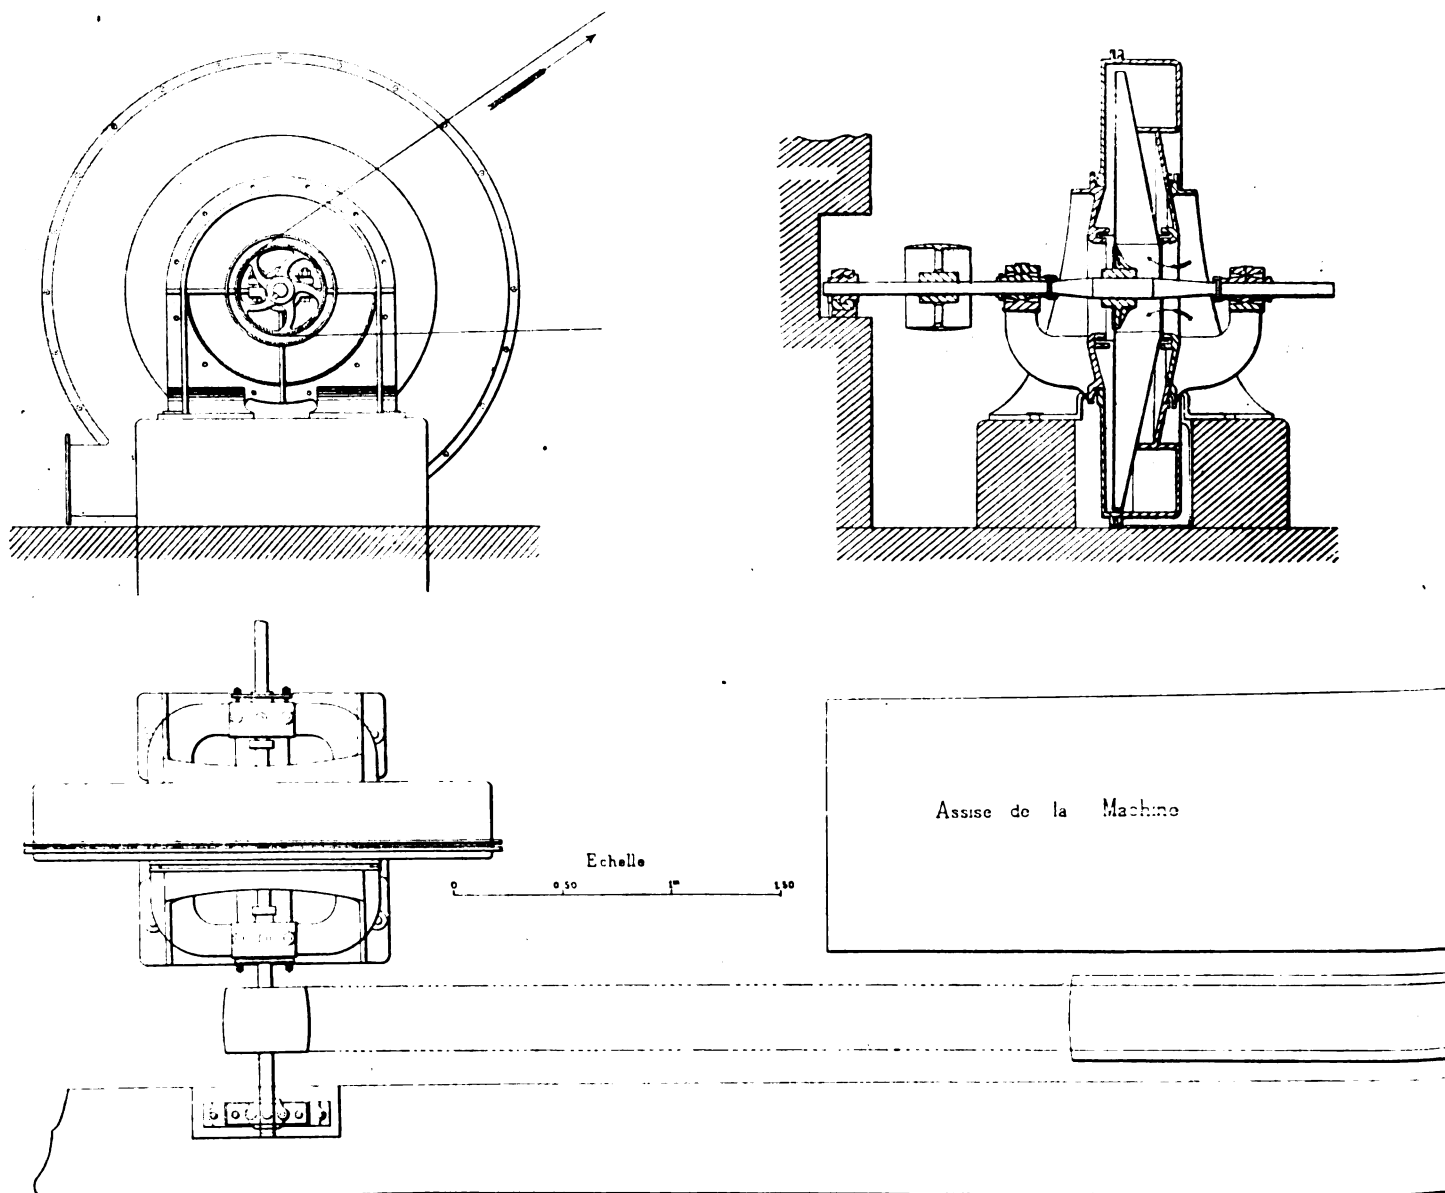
, 9, 10 et 11. — Élévation, coupe et plan d'un ventilateur système E. Farcot.
